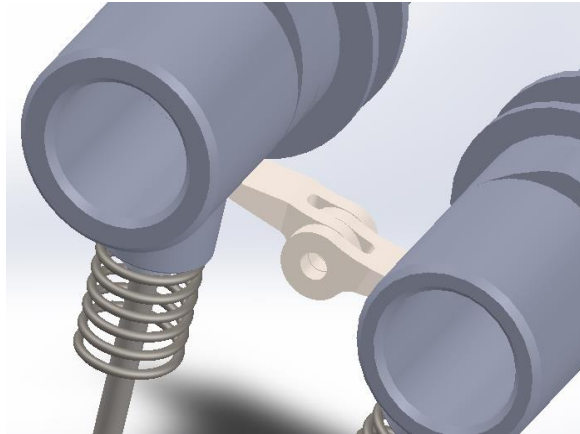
Posició de balancins en el ensamblatge de conjunt general
